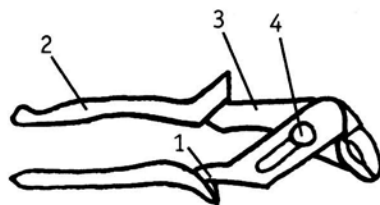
Ключи-клещи трубные переставные двухрычажные («галочки»): 1 — подвижный рычаг; 2 — чехол пластмассовый; 3 — неподвижный рычаг; 4 — грибовидный штифт-ограничитель
